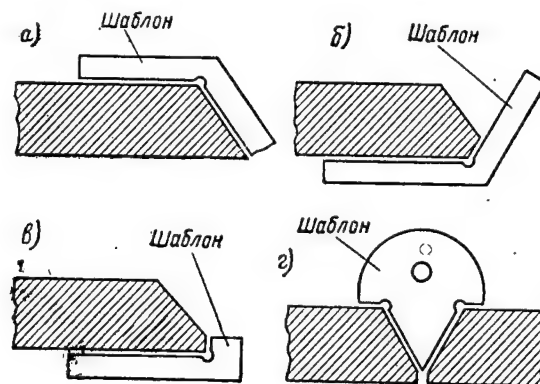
Проверка шаблонами разделки кромок для сварки:
